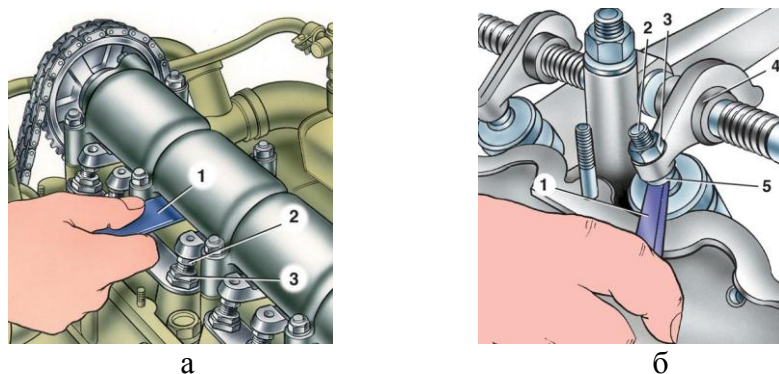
Проверка теплового зазора в ГРМ: а – ГРМ с роликовыми рычагами (рокерами); б – ГРМ с двуплечими рычагами (коромыслами); 1 – щуп; 2 – регулировочный винт; 3 – контргайка регулировочного винта; 4 – коромысло; 5 – наконечник нажимного винта
